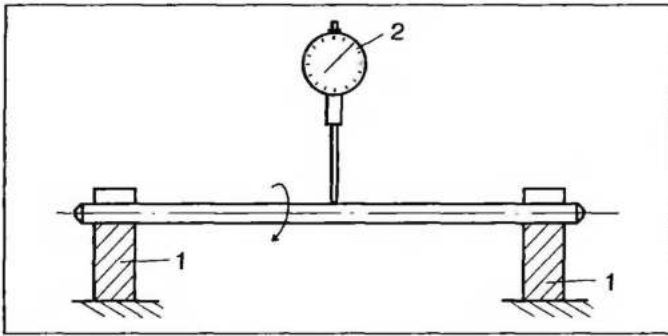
Схема проверки деформации толкающих штанг: 1 — призмы; 2 — индикатор
